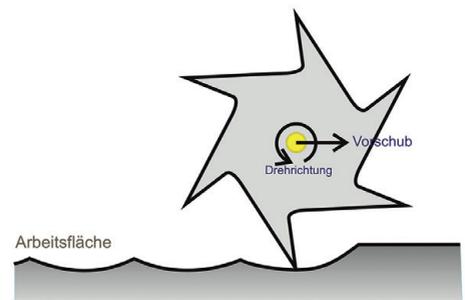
Beim Abschälen des Spanes erzeugen die Schneiden des Fräswerkzeugs ein wellenförmiges Profil
